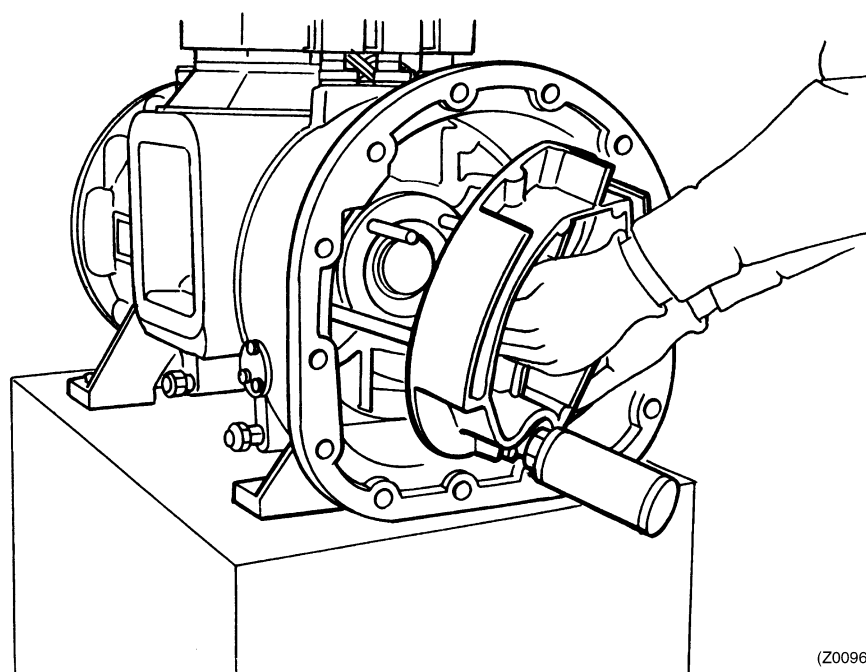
Снятие крепежной пластины главного держателя подшипников
